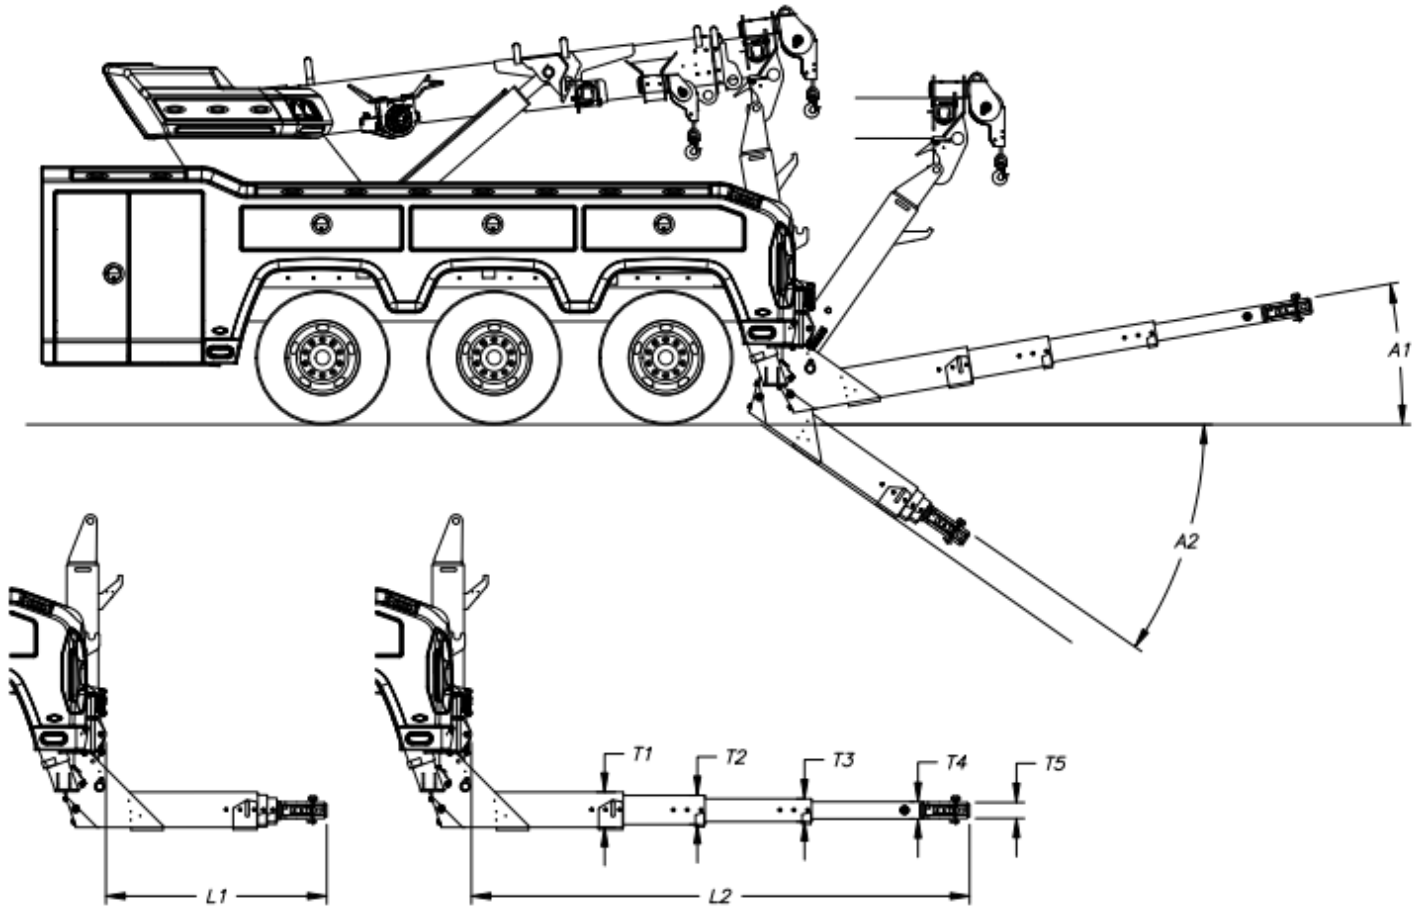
DIMENSIONS DU BRAS DE REMORQUAGE
